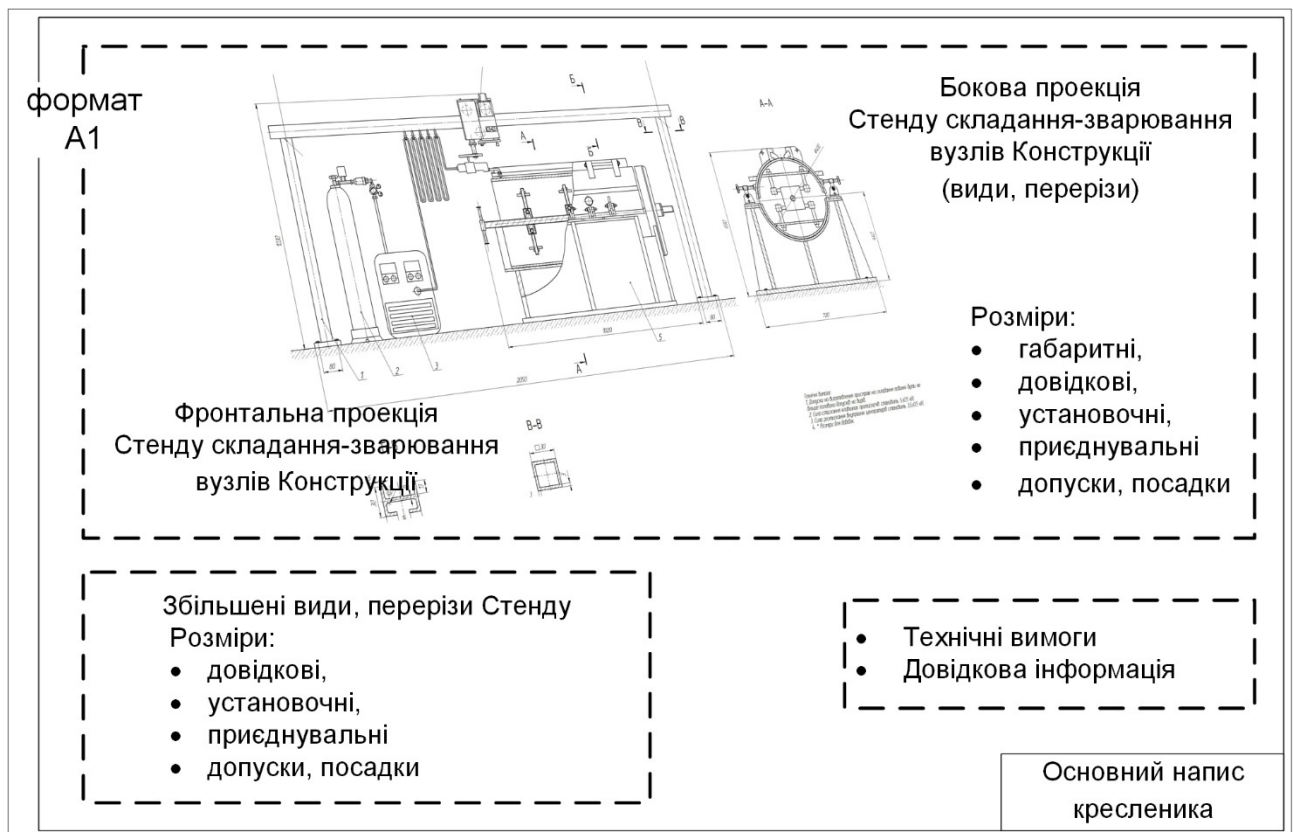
Рекомендована структура кресленника «Стенд для складання-зварювання вузлів {Конструкції}. Складальний кресленник»
